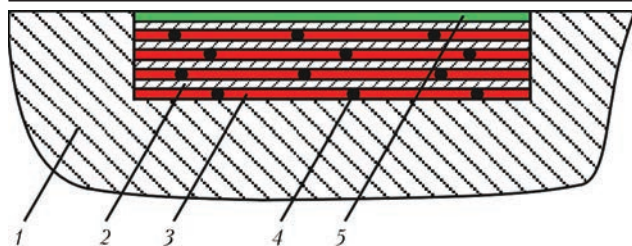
Клееварной метод восстановления посадочного места подшипника в корпусной детали: 1 — опора; 2 — многослой из тонколистовой стали 05кп; 3 — наполнитель межслойного пространства — анаэробный герметик; 4 — сварная точка; 5 — финишный слой композита
